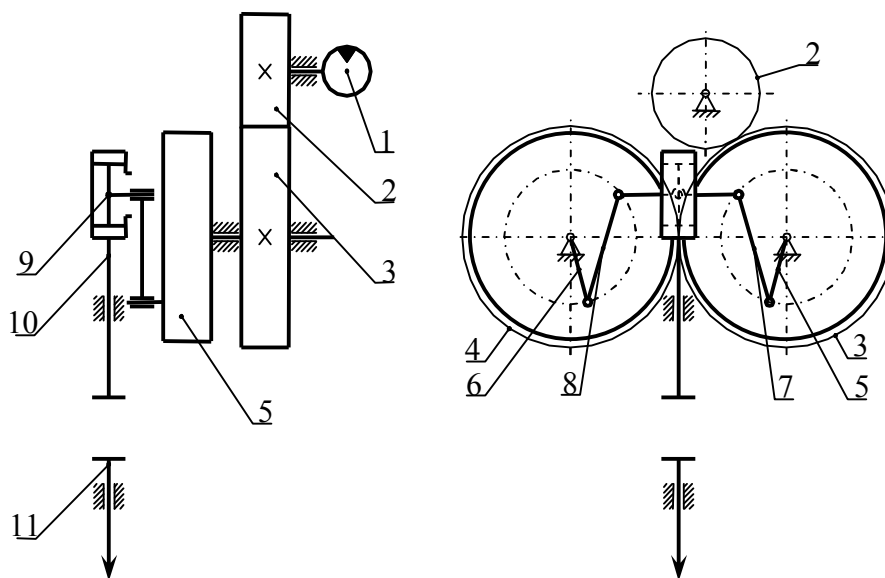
Кинематическая схема отбойного молота с ДКП-МПС с гидроприводом: 1 – гидродвигатель; 2 – шестерня; 3,4 – зубчатые колеса; 5,6 – маховики-кривошипы; 7,8 – шатуны; 9 – поводок; 10 – ползун – боек; 11 – инструмент
